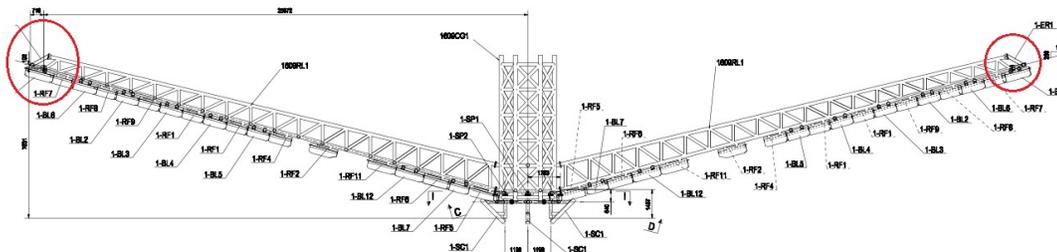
Vista de zona de extensión de rastras largas del Espesador THK-54. Adaptado de «Planos de montaje Modificación de Rastras», (13)
